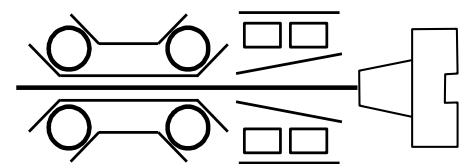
Типова компоновка передньої опори фрезерного верстату
